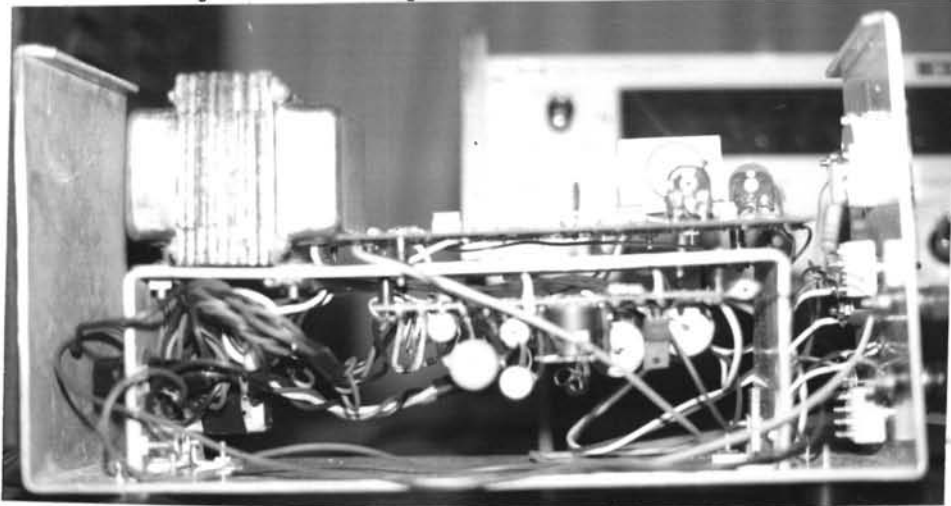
ภาพแสดงทางเดินสายของ Printed circuit board
